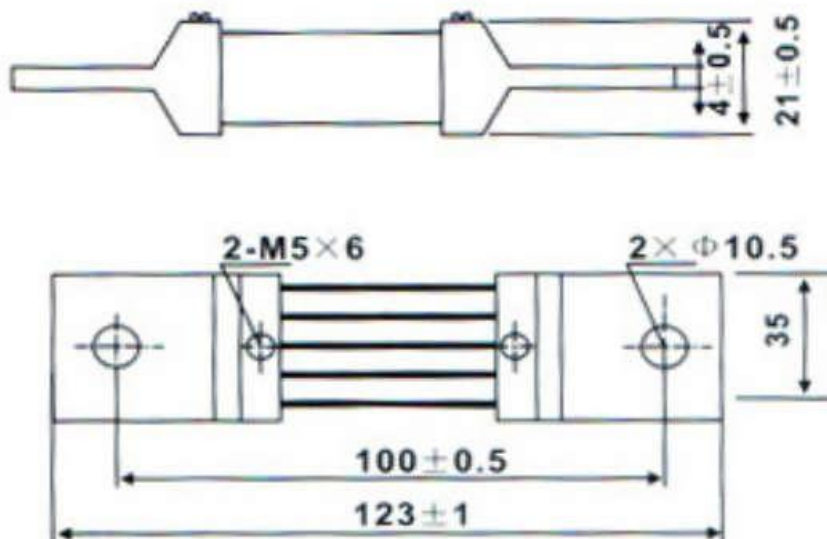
分流器外形尺寸图 Fig. 4 overall dimension of diverter
